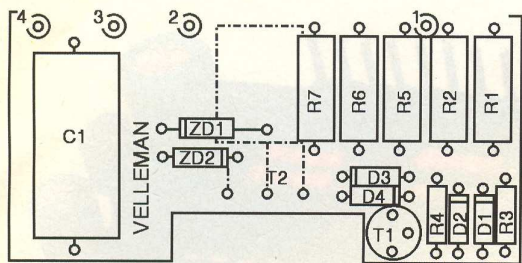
Desenul de amplasare a componentelor pe cablaj
